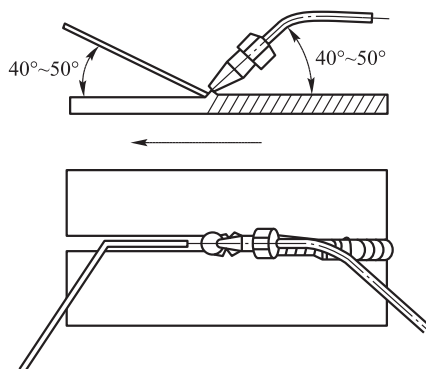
焊丝、焊炬与焊件的相对位置
